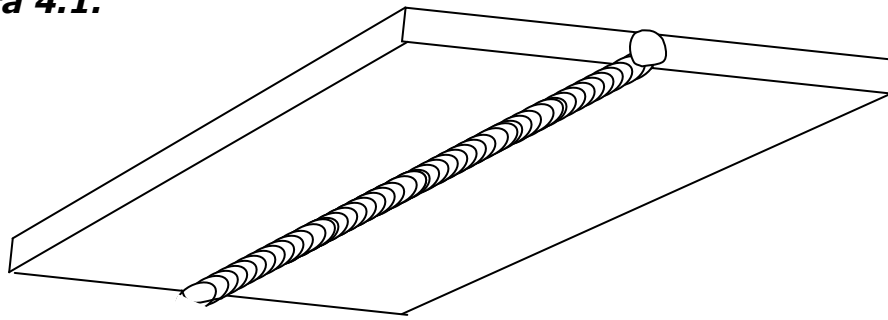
Soldadura de placas a tope en posición sobre cabeza.
